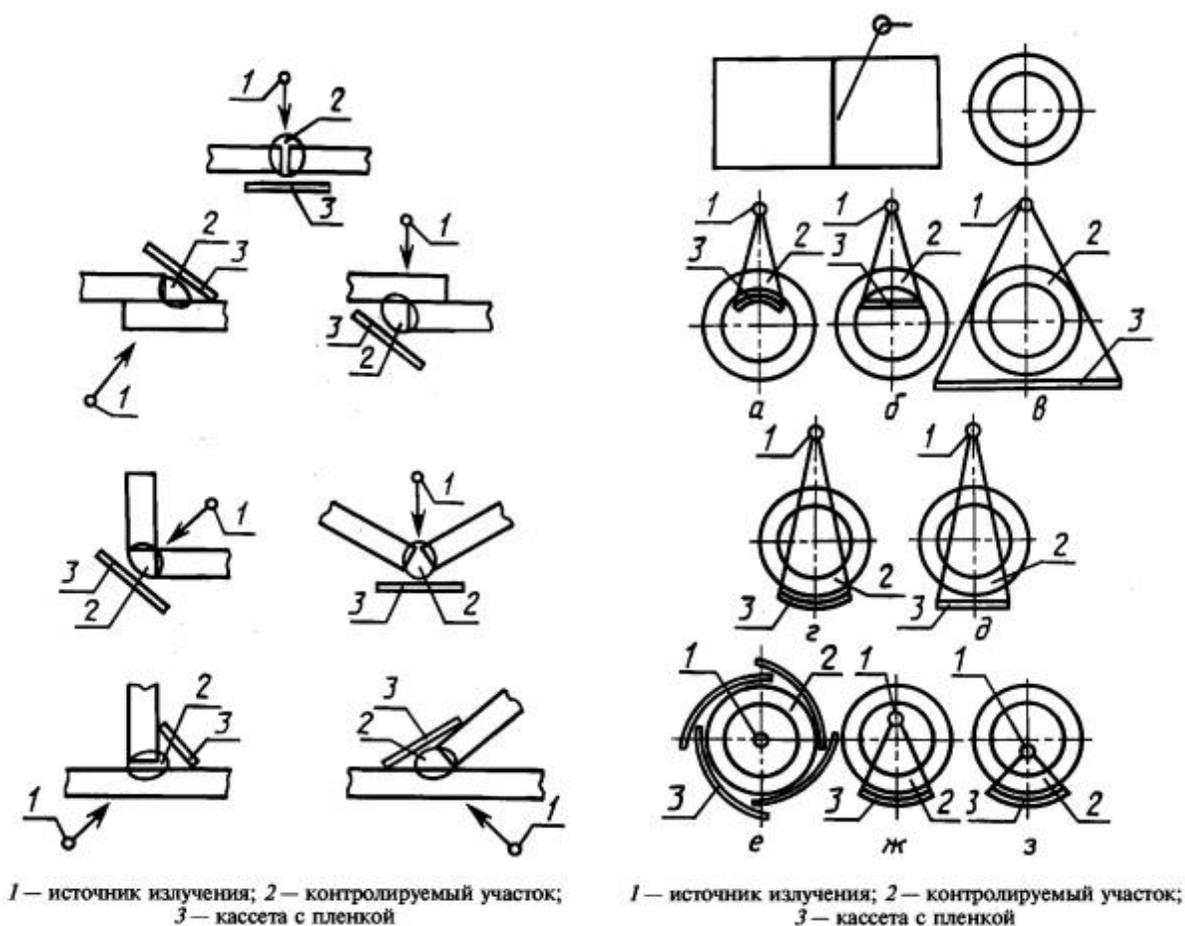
Схема контроля сварных соединений по ГОСТ 7512-82
